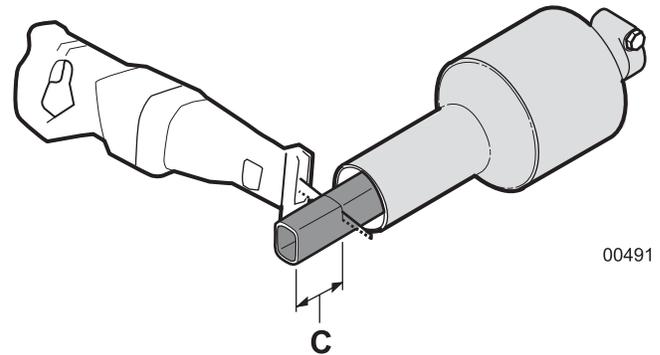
Coupez la longueur C des deux sections de l'arbre de prise de mouvement
